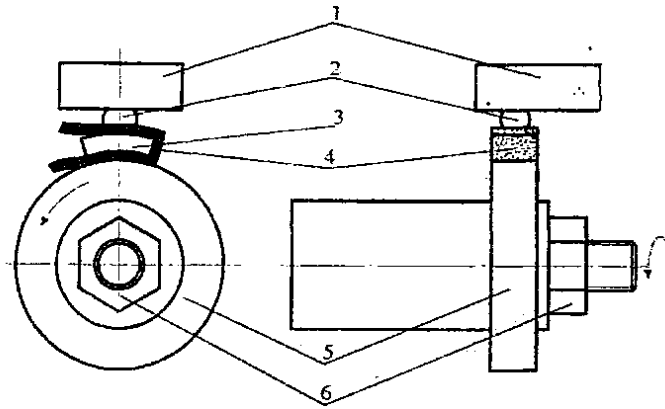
Схема установки абразивної шкірки на машині тертя:
